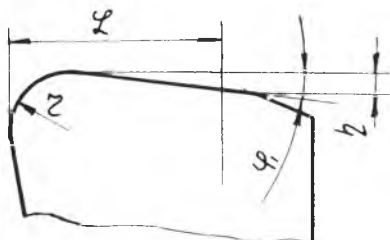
Элементы геометрии проходного упорного резца для расчета размеров канавки при точении резцами 1-го и 2-го типа (рис. 7).
